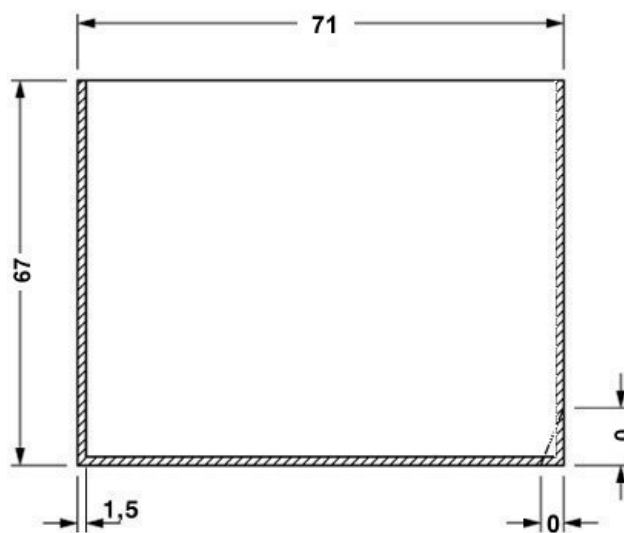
Dimensioned drawing 4 - valid for PCB 7; 8; 11 and 12, see Explosion drawing.
